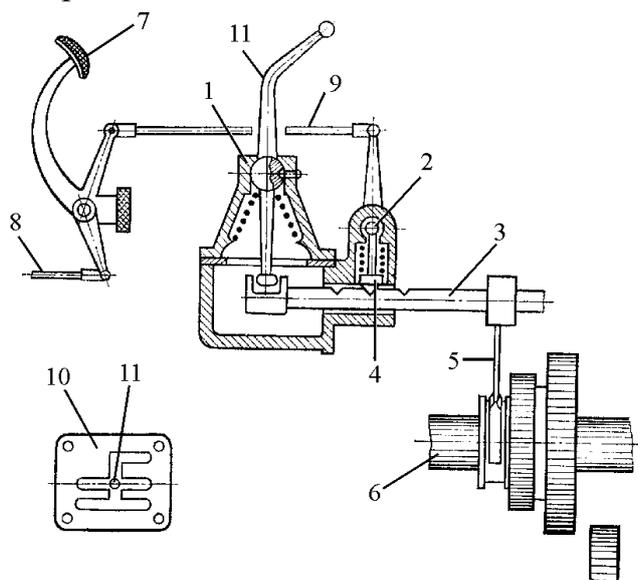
Механизм переключения передач: 1 – шаровая опора; 2 – валик; 3 – ползун; 4 – фиксатор; 5 – вилка; 6 – вал с шестернями КП; 7 – педаль сцепления; 8 – тяга управления сцеплением; 9 – тяга управления фиксатором; 10 – направляющая рычага переключения передач; 11 – рычаг переключения передач
